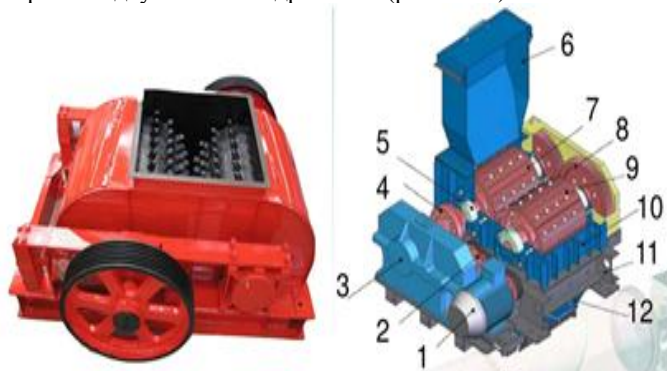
Валковая дробилка: 1-электродвигатель; 2-ременная передача; 3- редуктор; 4- муфта; 5- опора подшипниковая; 6- бункер; 7-
